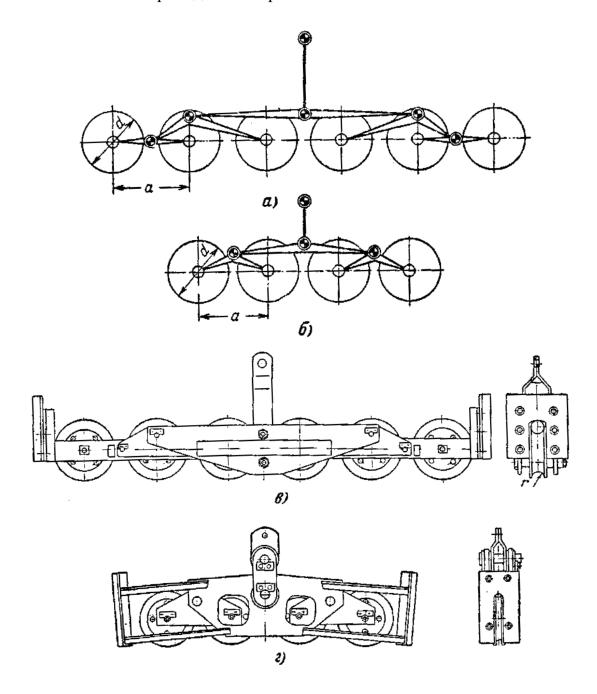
Роликовые балансирные подвесы для больших переходов: a — кинематическая схема шестироликового подвеса;  $\delta$  — кинематическая схема четырехроликового подвеса;  $\epsilon$  — общий вид шестироликового повеса;  $\epsilon$  — общий вид четырехроликового подвеса
